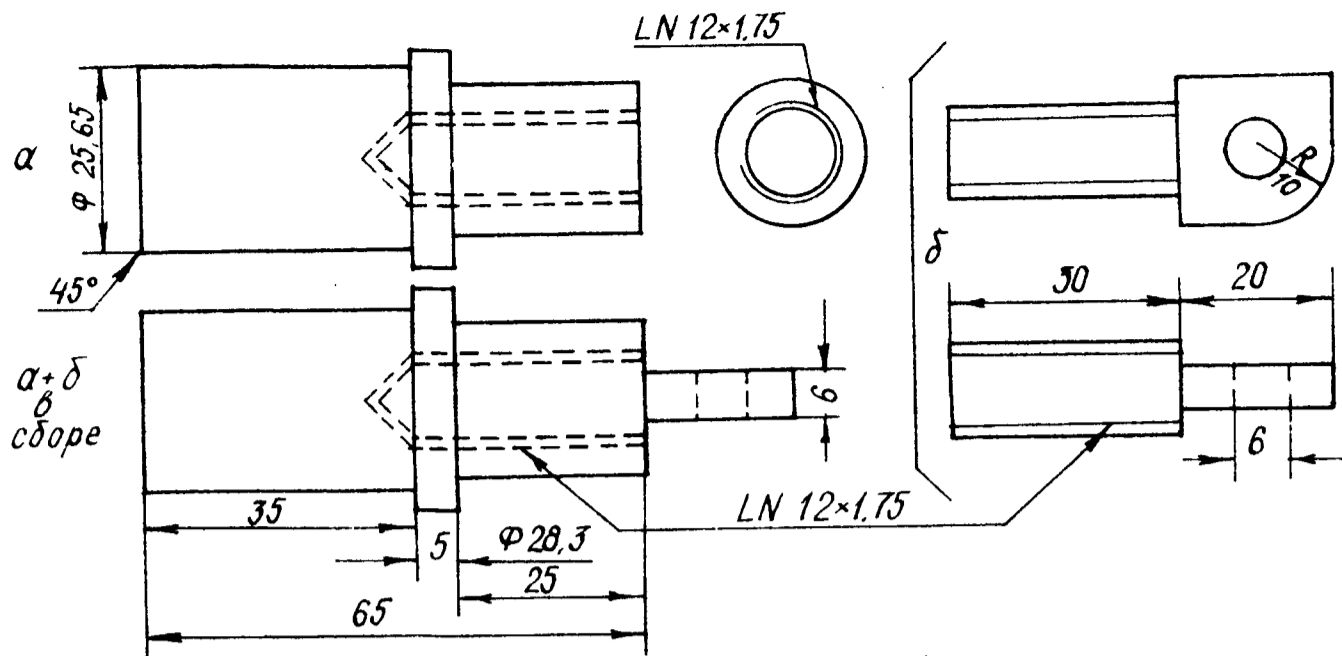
Нижний короткий вкладыш сборный (из деталей а и б)
